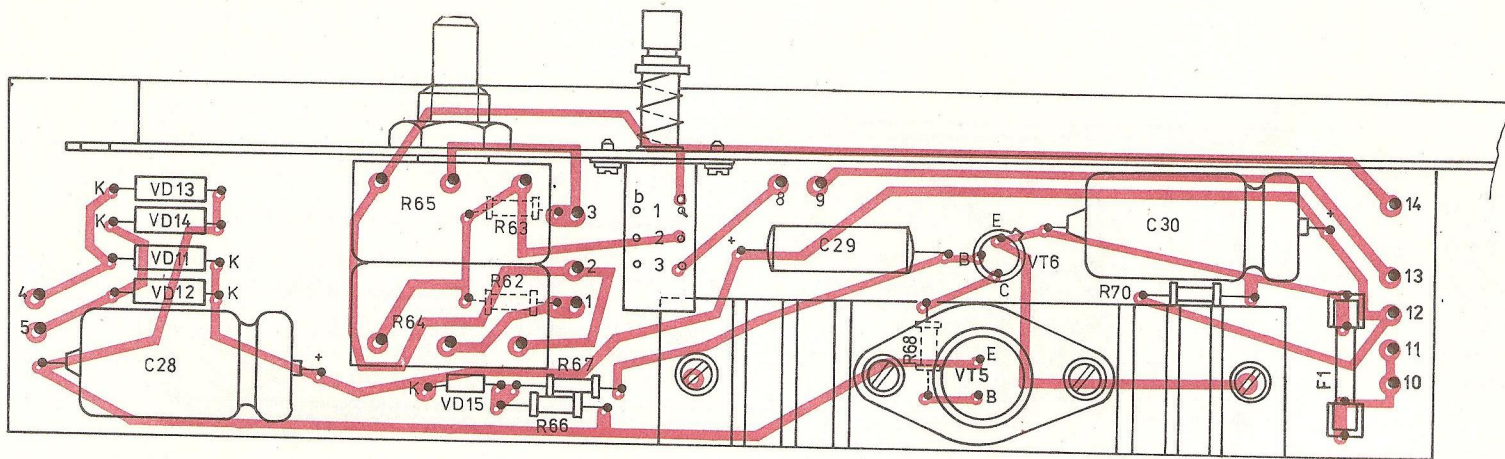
Deska směšovací 3AK 061 39 (strana spojů)
